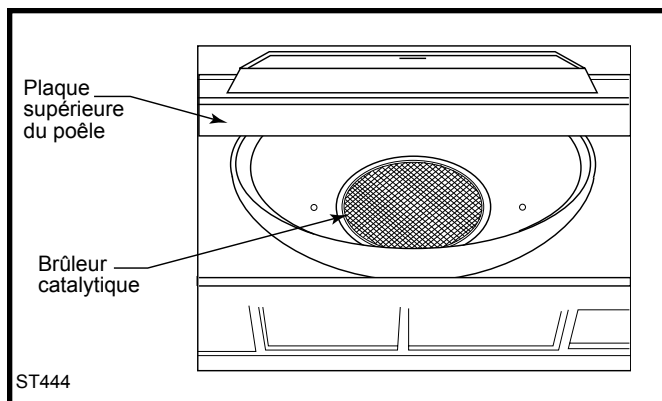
Retirer l'ensemble de réfractaires avec soins.
